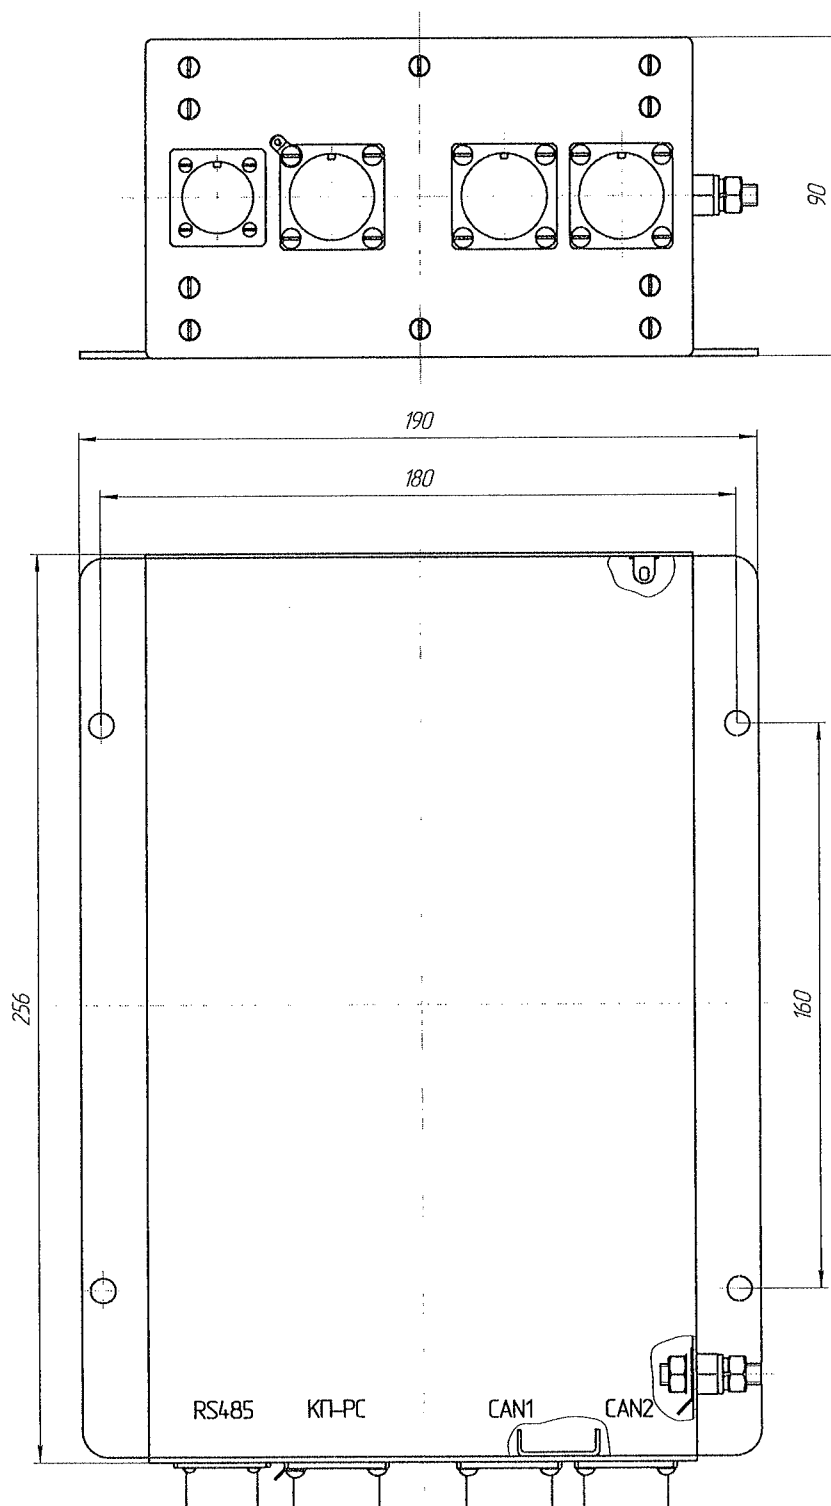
Внешний вид и габаритные размеры блока
